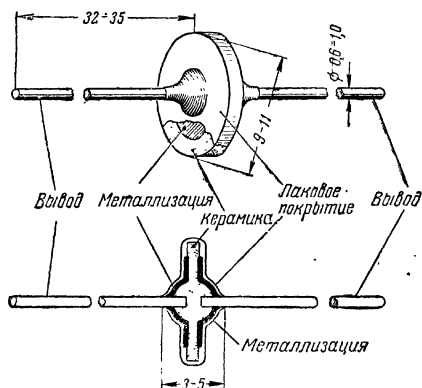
Общий вид и разрез керамического дискового конденсатора типа КДК-3. Часть лакового покрытия (верхний рисунок) удалена с поверхности конденсатора
